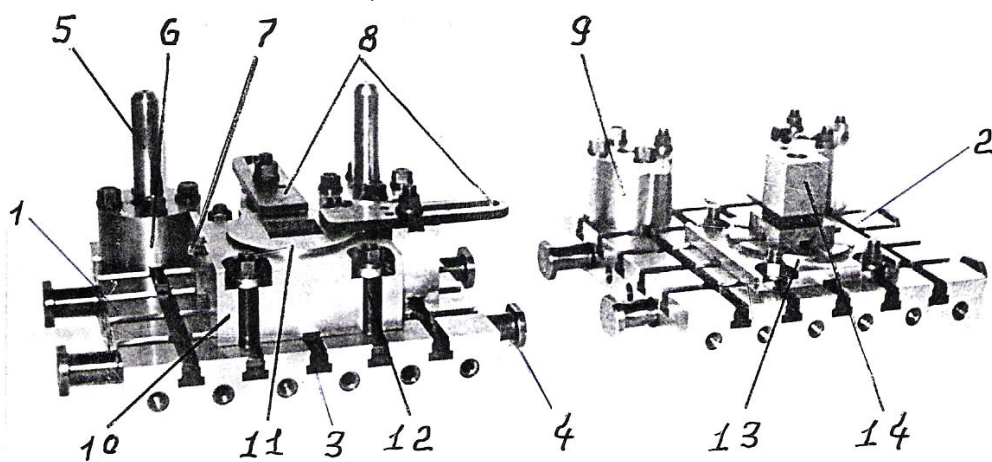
Гидрофицированное универсально-сборное приспособление для обработки кронштейна на фрезерном станке
